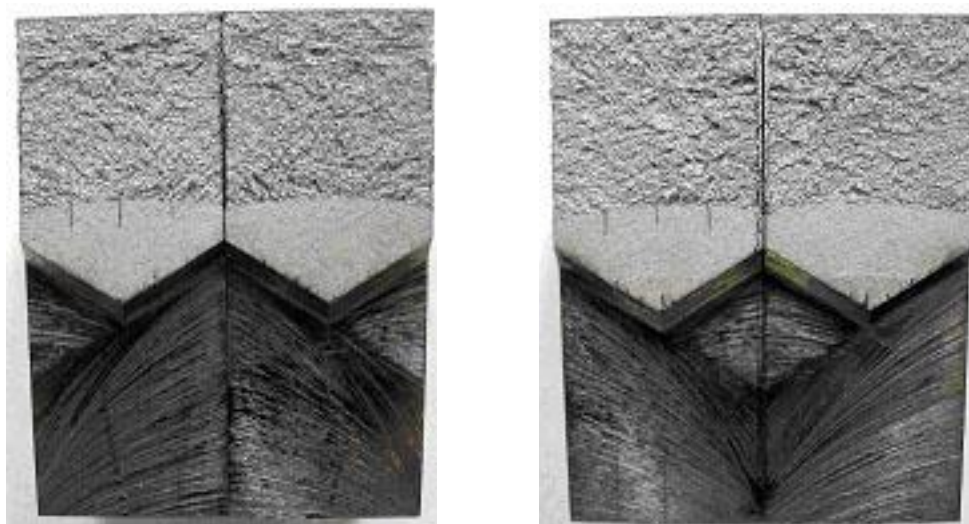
Типичные изломы образцов плавки 522922 (0,64% С)
